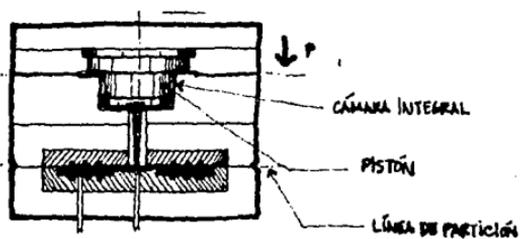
Esquema de un molde de transferencia con cámara integrada.
